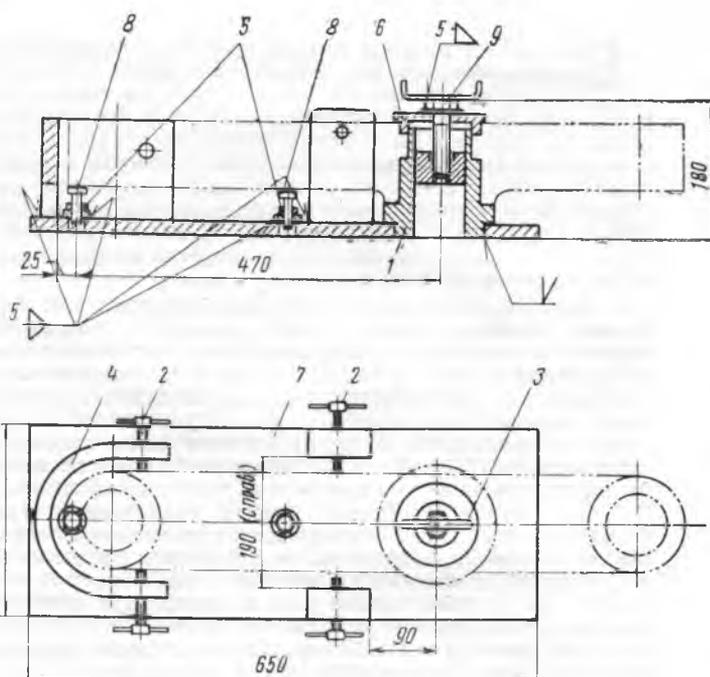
Схема приспособления для расточки балансира и щек кривошипов тракторов ТДТ-60 (75):
